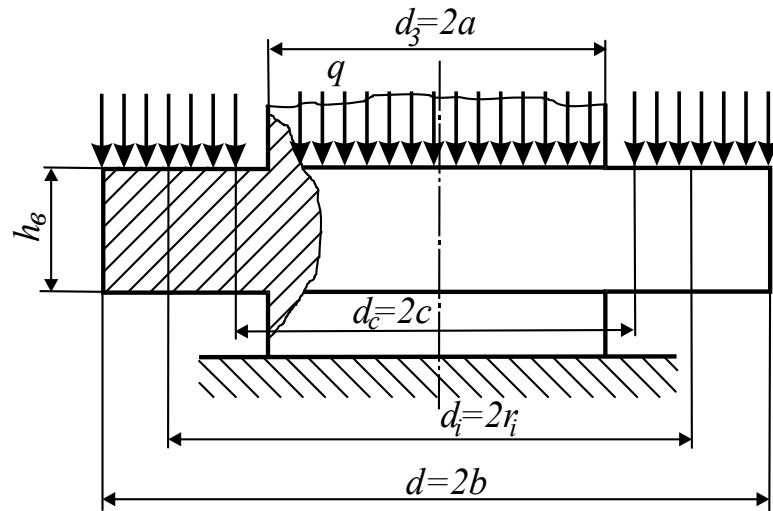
Расчетная модель витка резьбы в виде круглой пластинки
